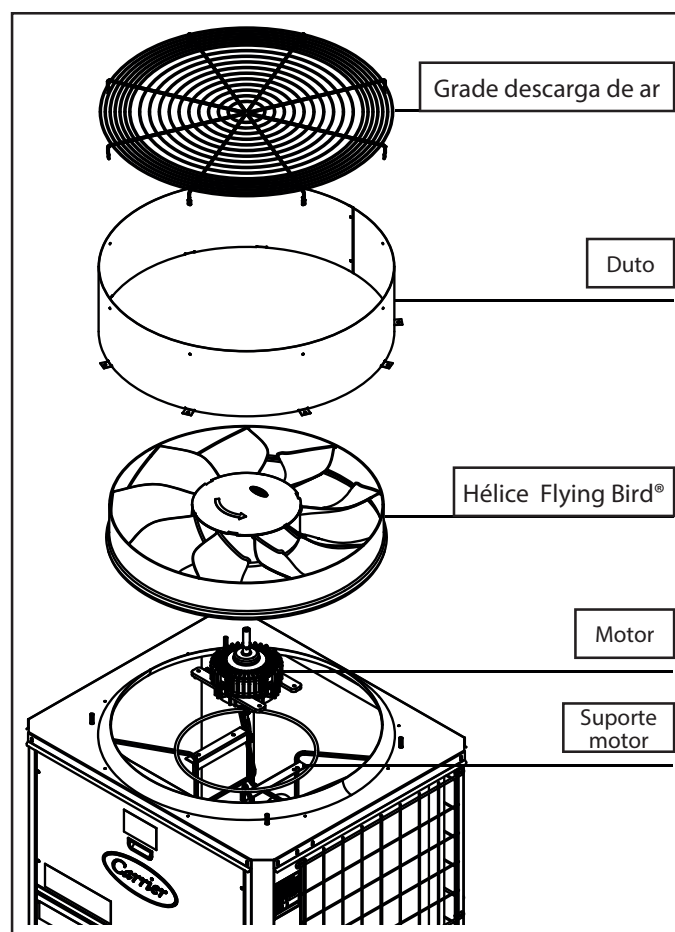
Vista explodida conjunto ventilador das un. condensadora 38EX/38EV e Hélice Flying Bird®
